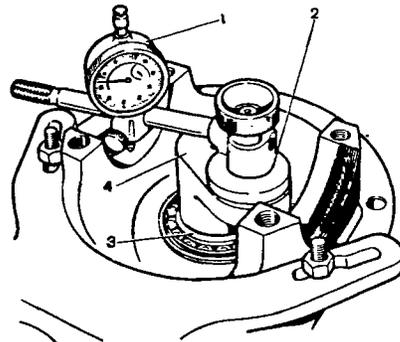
Определение толщины регулировочного кольца ведущей шестерни: 1 - индикатор; 2 - приспособление А.95690; 3 - задний подшипник ведущей шестерни; 4 - оправка А.70184
